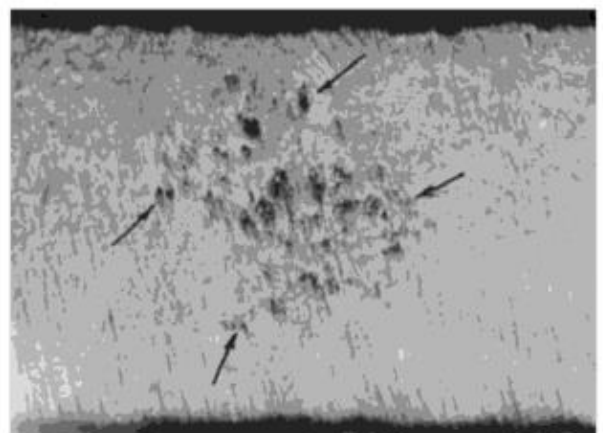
Трещина, развившаяся из микрорыхлот в процессе механической обработки литой заготовки из сплава АЛ9
